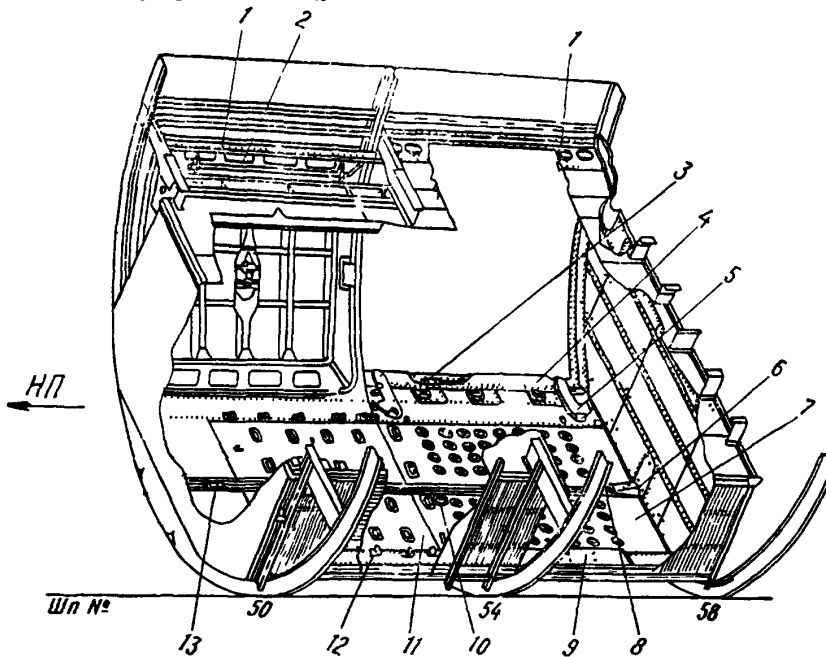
Задний грузовой отсек самолета Як-42 (контейнерный вариант): 1 — верхний рельс крышки загрузочного люка; 2 — крышка загрузочного люка; 3 — педаль механизма перестановки пальца каретки; 4 — фартук; 5 — направляющая; 6 — упор заднего механизма натяжения цепи; 7 — шариковая панель пола; 8 — каретка; 9 — бортовой ограничитель; 10 — поршень механизма фиксации; 11 — роликовая панель пола; 12 — швартовочный узел; 13 — передний механизм натяжения цепи
